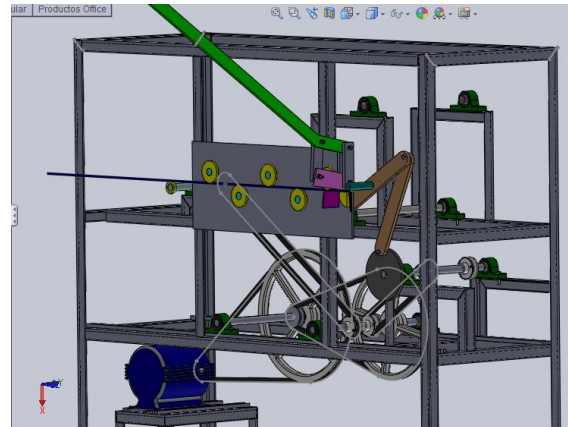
Diseño de la máquina estribadora utilizando SolidWorks
